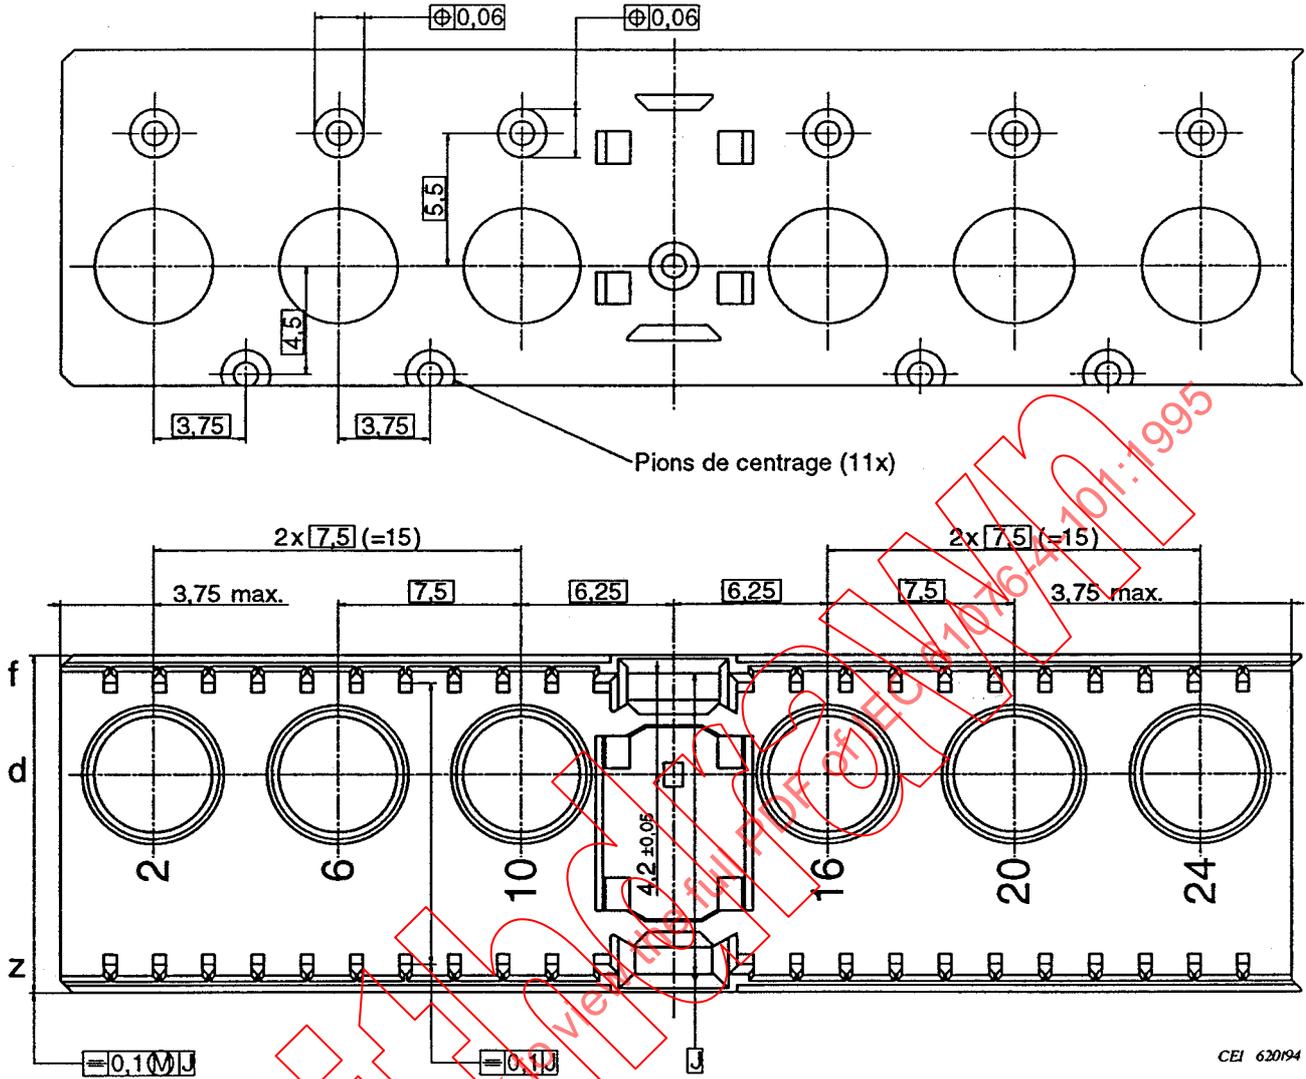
Dimensions du modèle L, module d'embase 50 mm avec six contacts spéciaux
